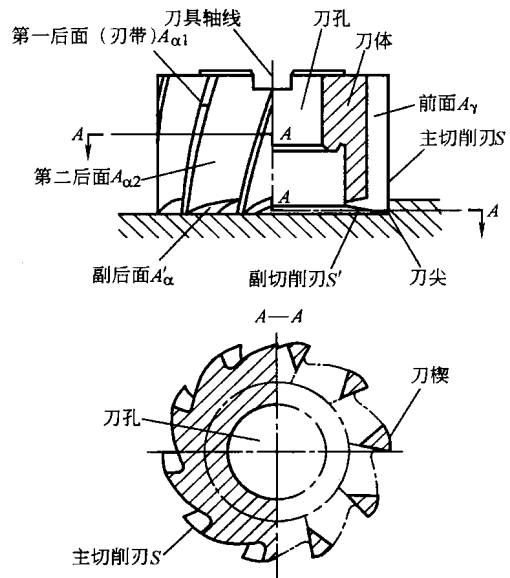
套式立铣刀切削部分上的切削刃和刀具表面
